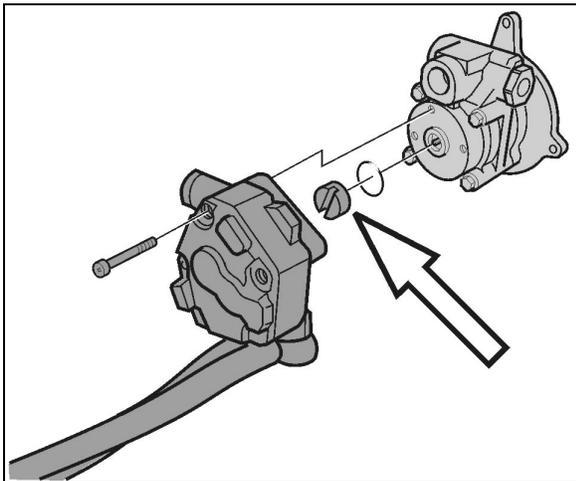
ARBRE D'ENTRAÎNEMENT DE LA POMPE À CARBURANT
